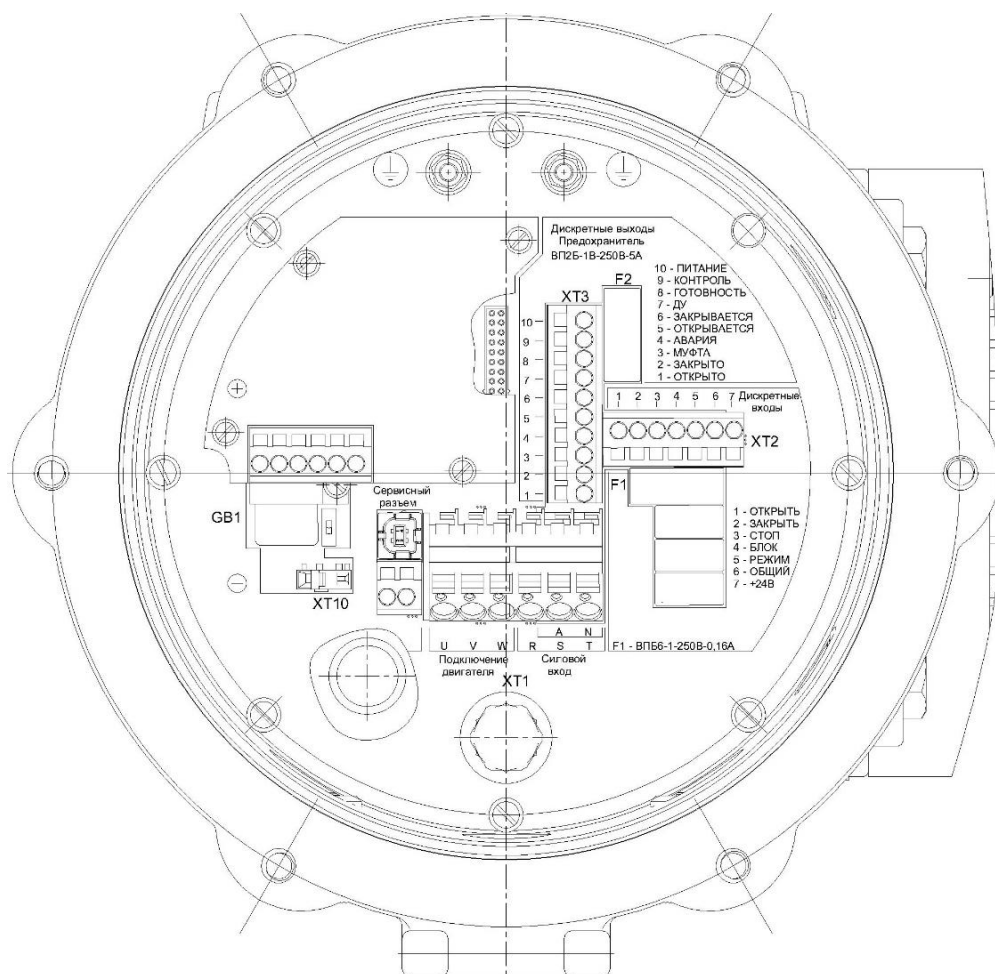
а – Типовой внешний вид бокса РэмТЭК
